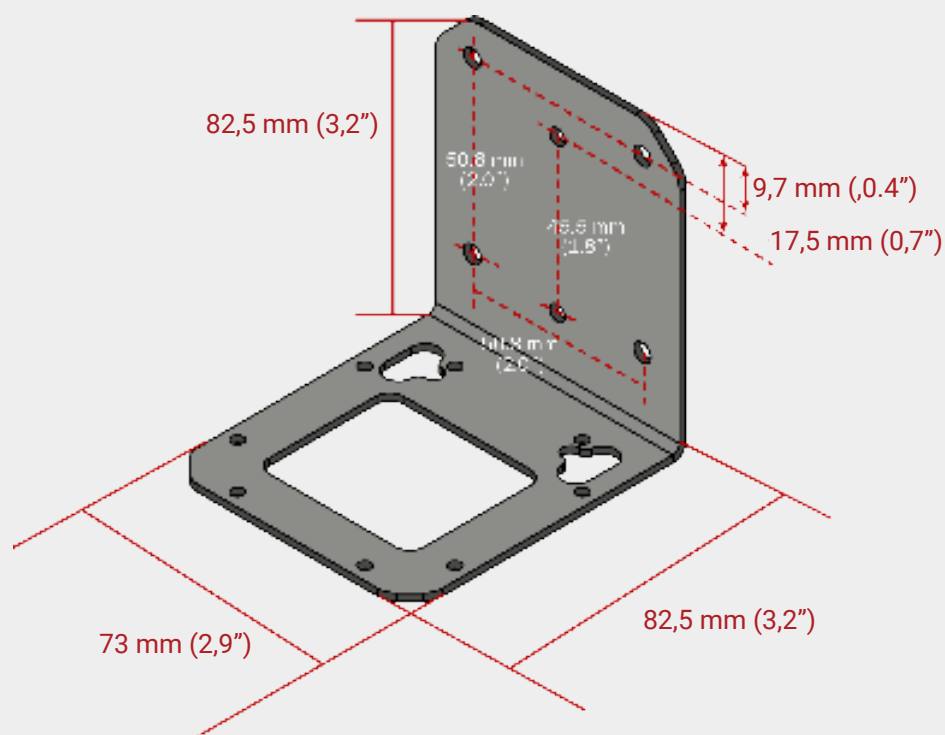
Dimensioni della staffa per montaggio a parete CRA-WMB4-C286
